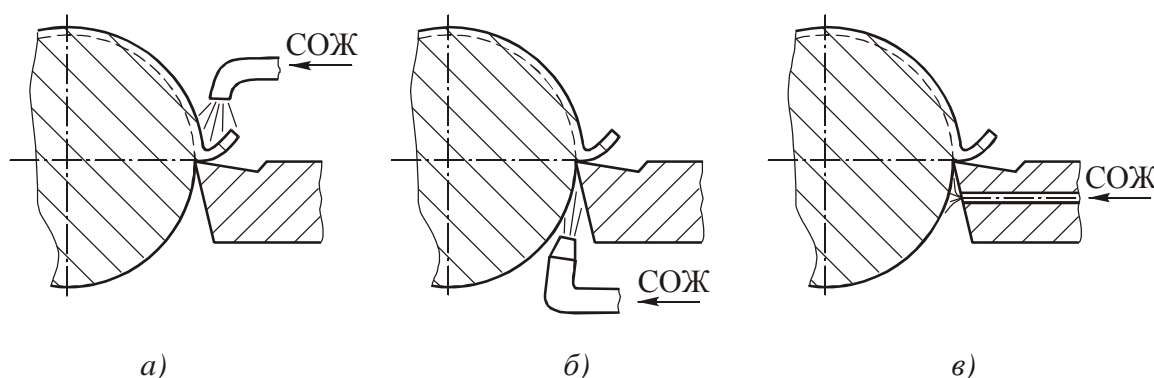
Способы подачи СОЖ в зону резания: *а* – поливом сверху; *б* – напорной струей со стороны задней поверхности; *в* – через отверстие в инструменте
